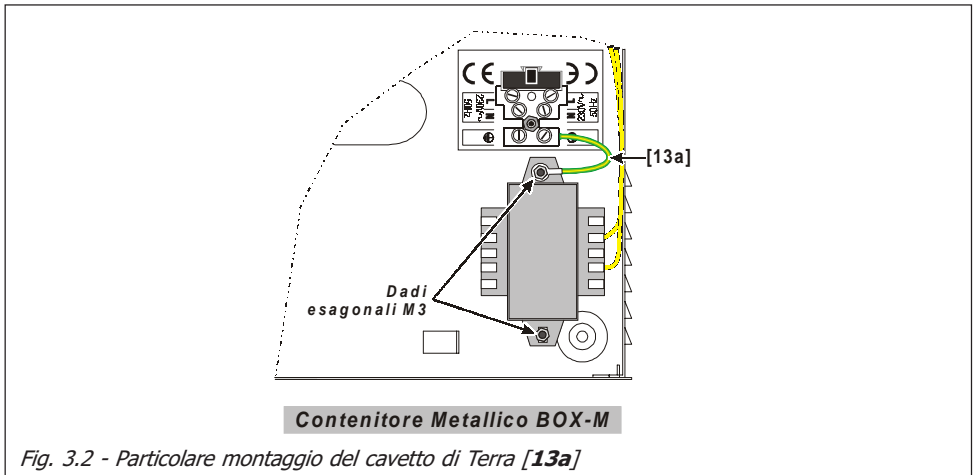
Particolare montaggio del cavetto di Terra [13a]
